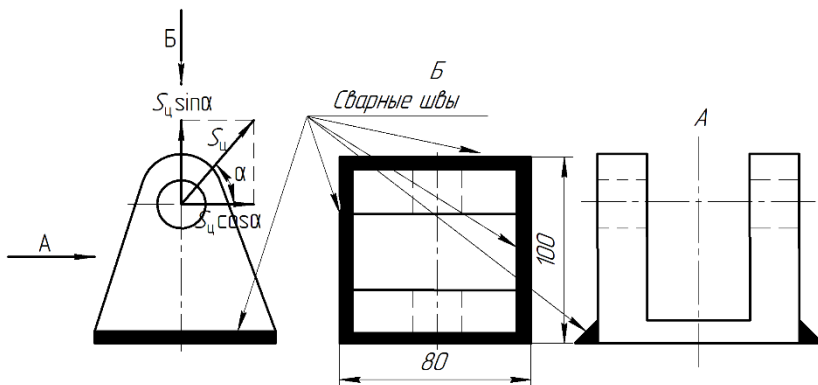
Расчетная схема для проверки сварных швов на прочность
